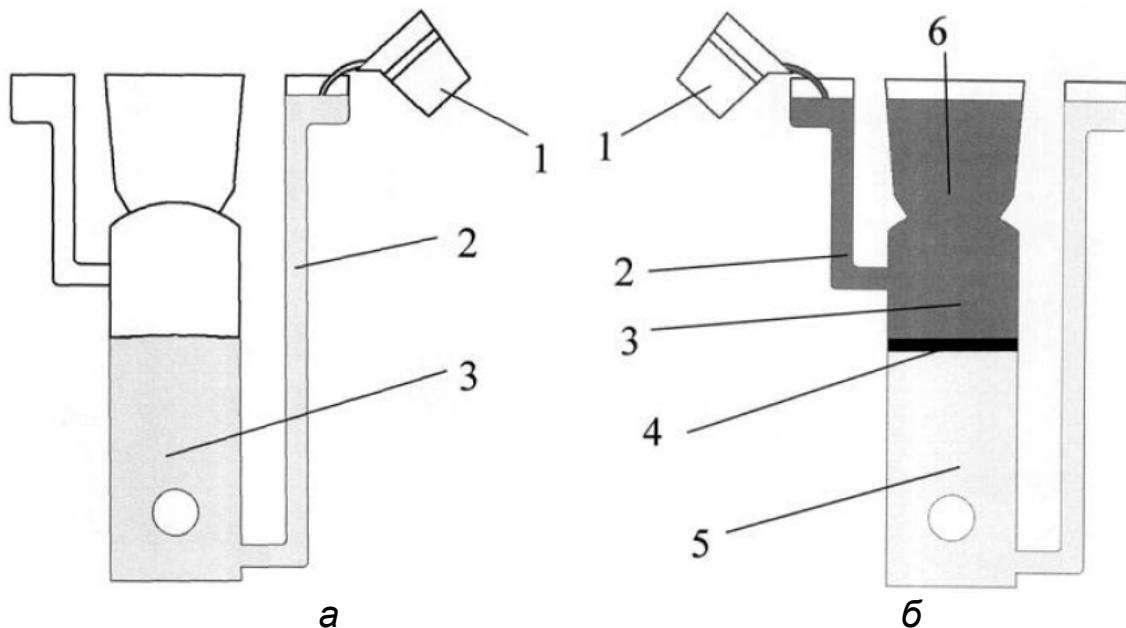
Схема виготовлення біметалевих виливків [8, 9].
